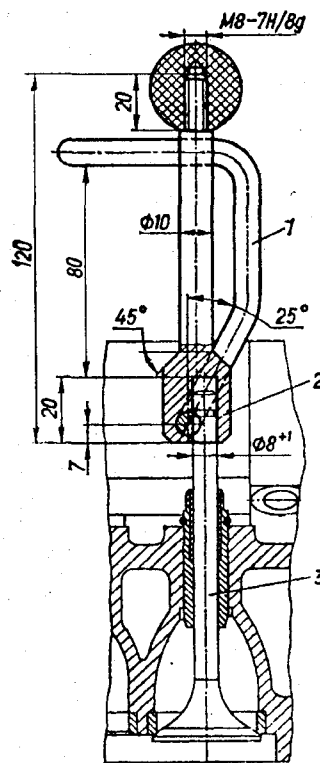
Приспособление для притирки клапанов: 1 – зажим; 2 – оправка; 3 – клапан
